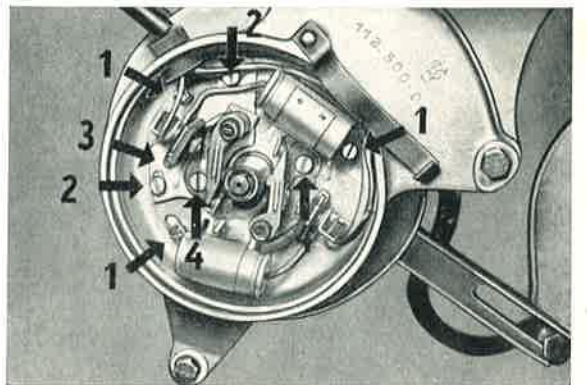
1: Klemmschrauben der Grundplatte, 2: Klemmschrauben der drehbaren Platte des 2. Unterbrechers, 3: Einstellschraube für Platte des 2. Unterbrechers, 4: Klemmschrauben der Kontaktträger beider Zylinder.
